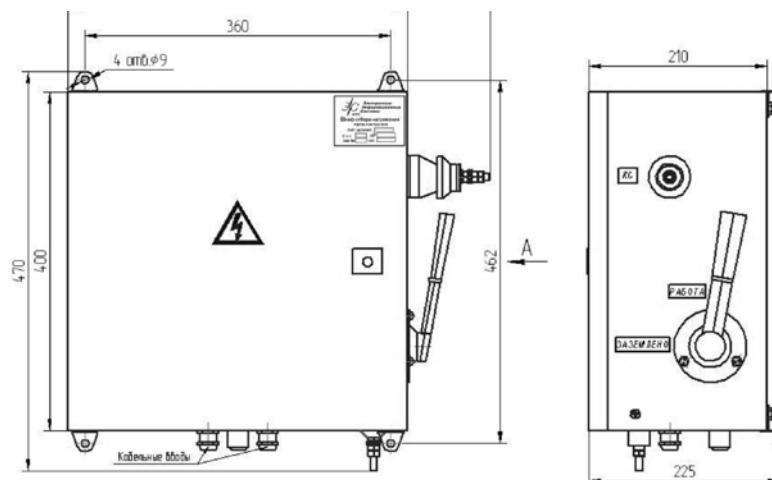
Габаритно-присоединительный чертеж Фильтр-ШОН.
